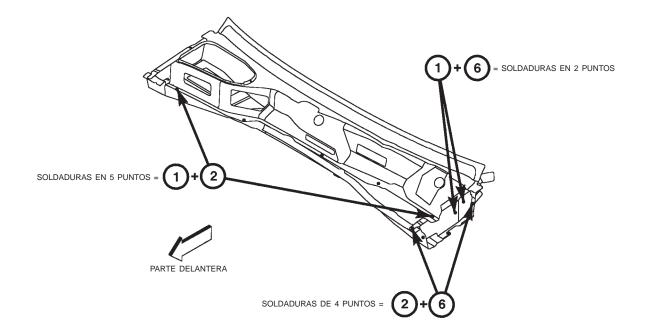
CONJUNTO DE CAMARA IMPELENTE
